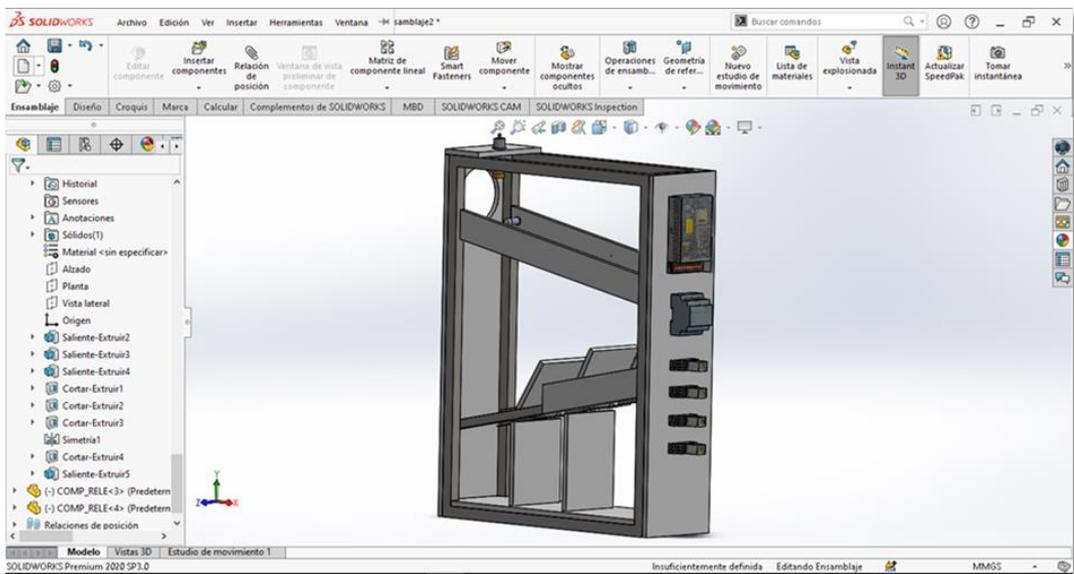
Proyecto ensamblaje – Solidworks (Vista 1)
